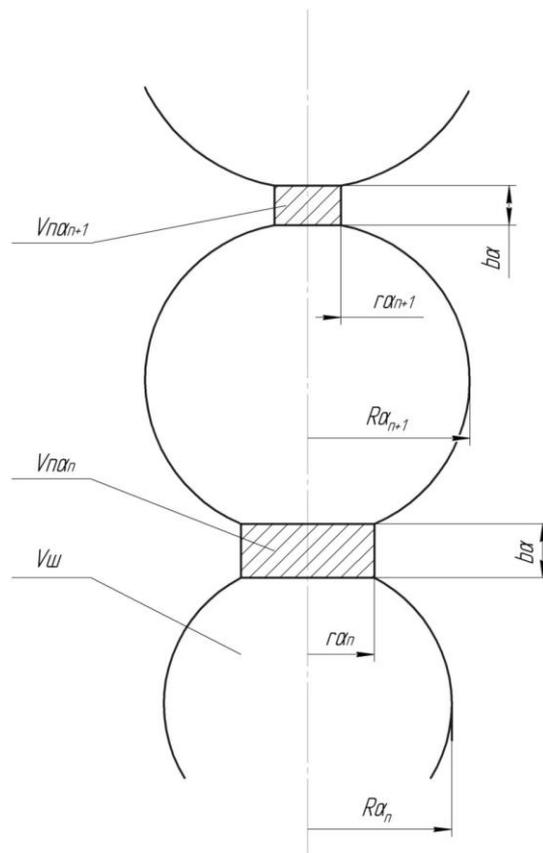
Сечение заготовки во время прокатки с углублением впадины.
